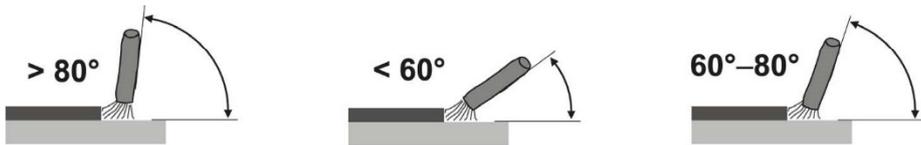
Напрямок зупинки дуги під час ручного дугового зварювання («ММА»).
